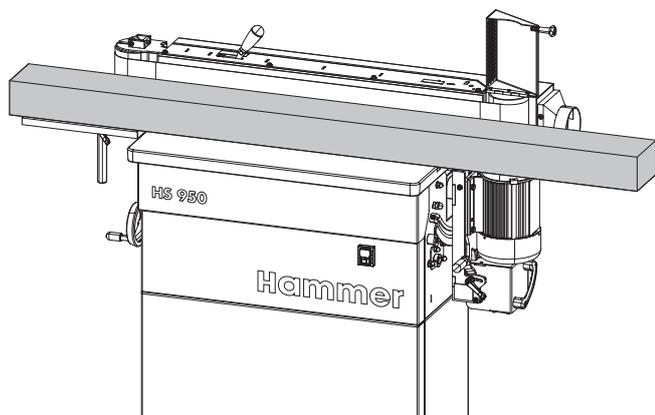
Шлифование длинных обрабатываемых деталей
